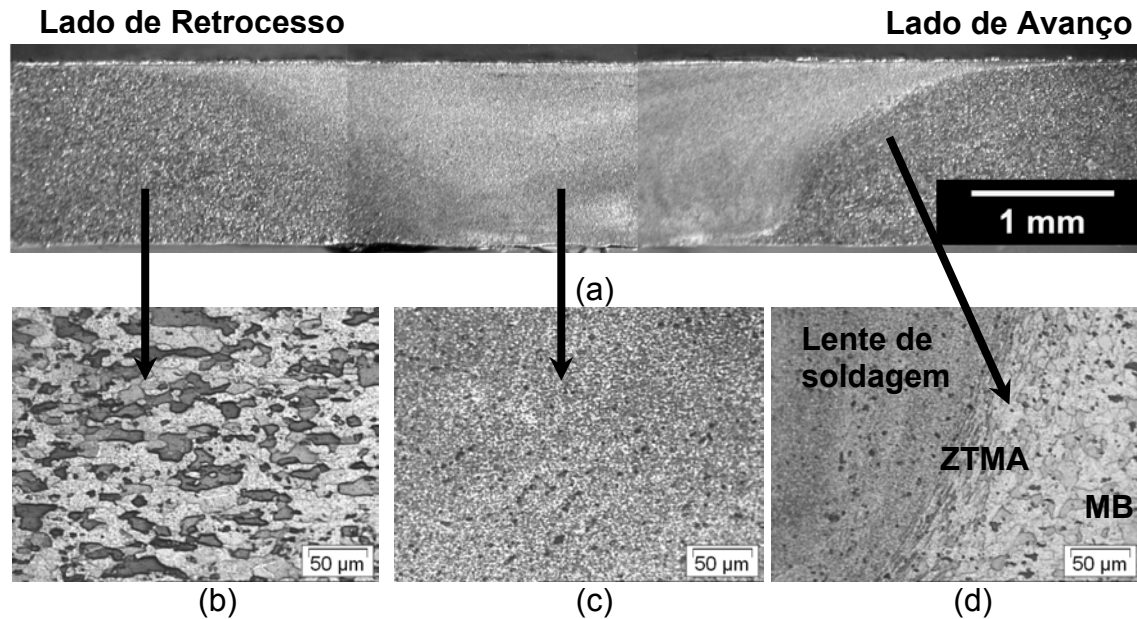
(a) Microestrutura da liga 2024-T351, soldada por FSW, corte transversal. Regiões microestruturais da junta soldada. (b) Metal base. (c) Lente de soldagem. (d) ZTMA, zona termomecanicamente afetada.
